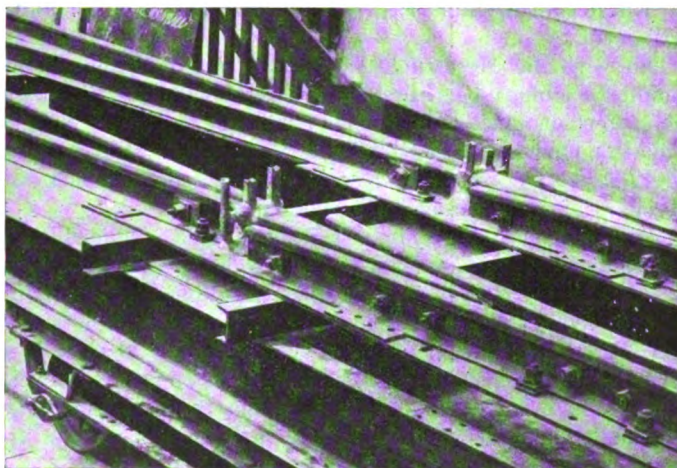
Herzstücke, nach dem Zwischengußverfahren verschweißt, im Rohzustand.
